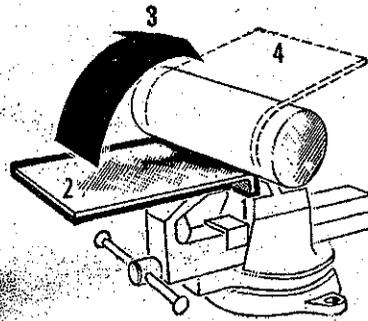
Fabrication du corps du silencieux de J. Vignolles.
